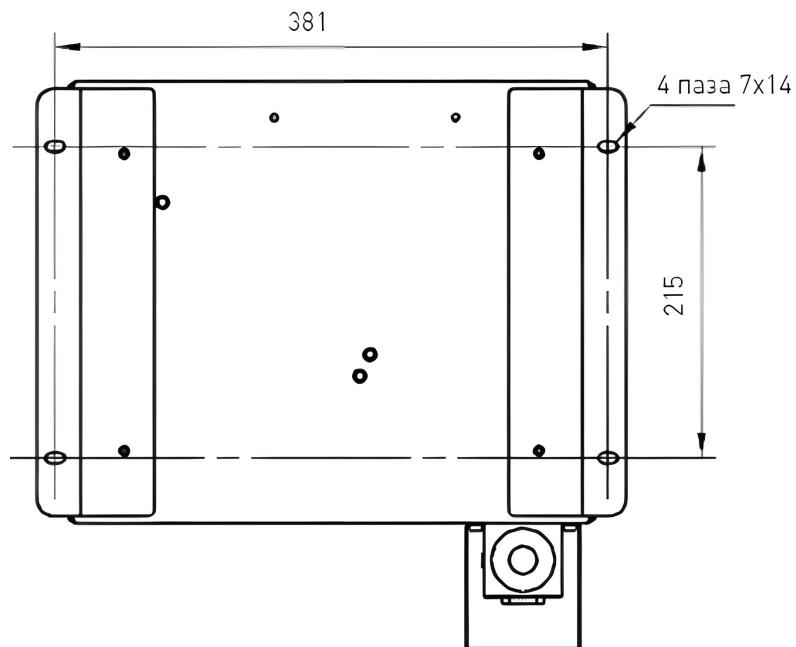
Схема нижнего монтажа газовой консоли.
